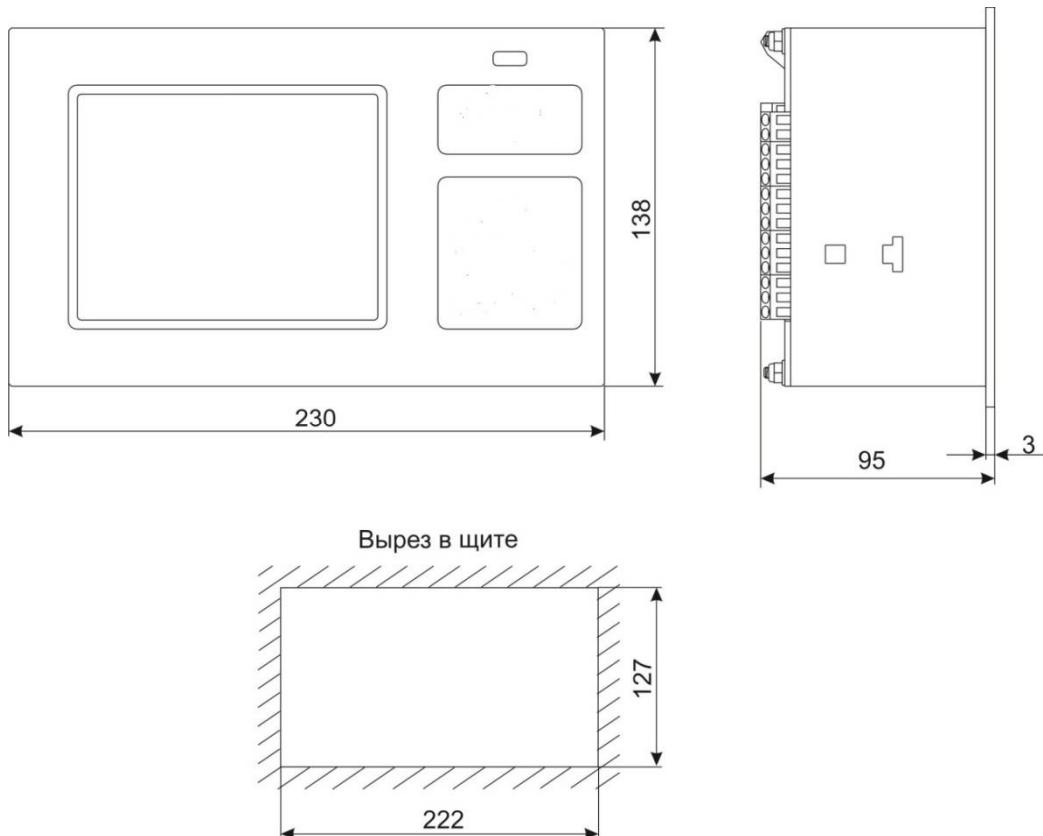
Габаритные размеры основного блока прибора Термодат-29Е6/..../F
